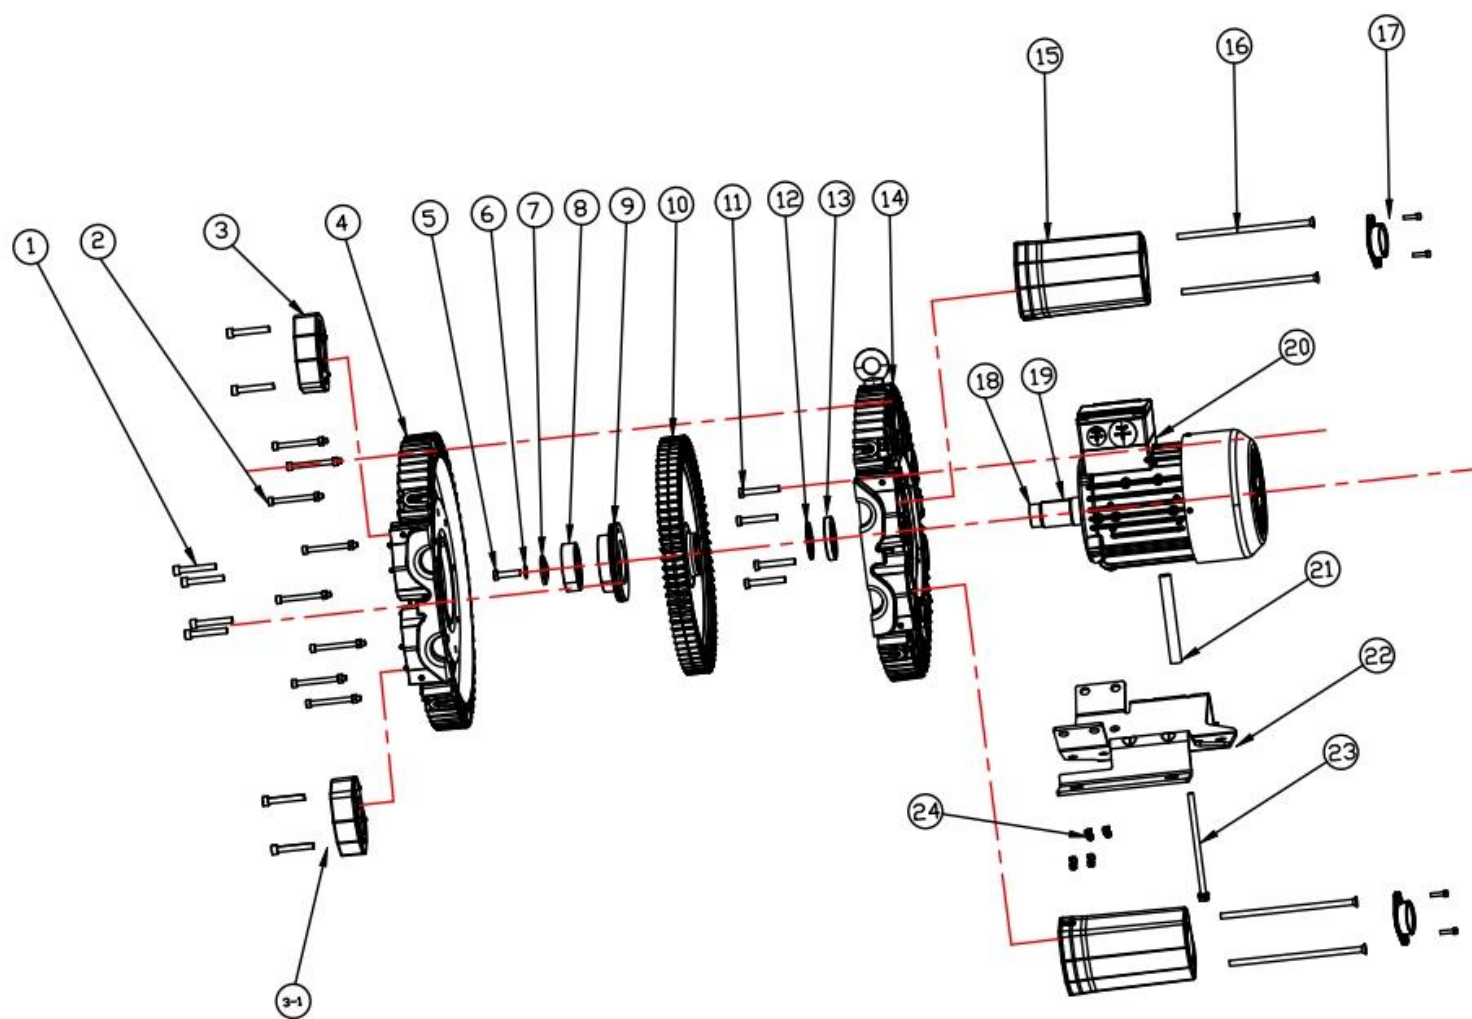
Деталировка одноступенчатых воздуходувок 4RB
